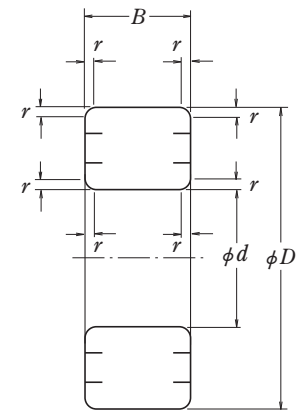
Äußere Abmessungen für Radialkugel- und rollenlager
